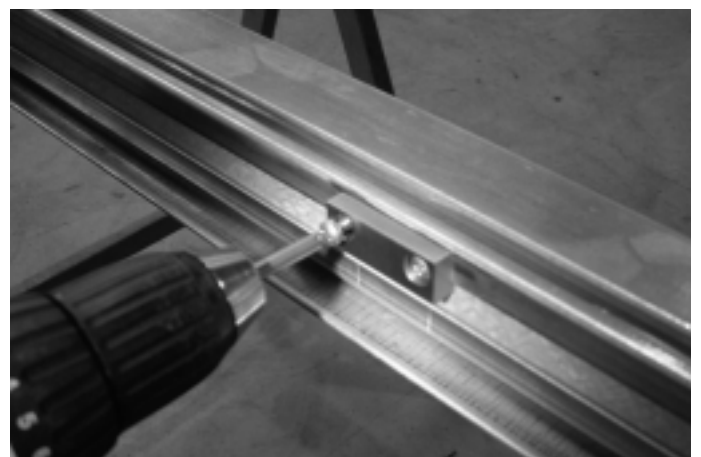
Befestigung Falzsicherungsklötze mit Linsenschrauben 550.375
